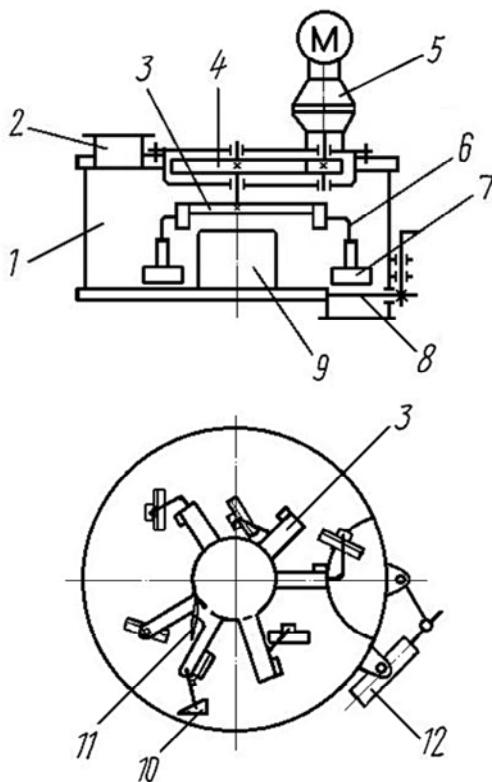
Конструктивная схема роторного циклического бетоносмесителя роторного типа
